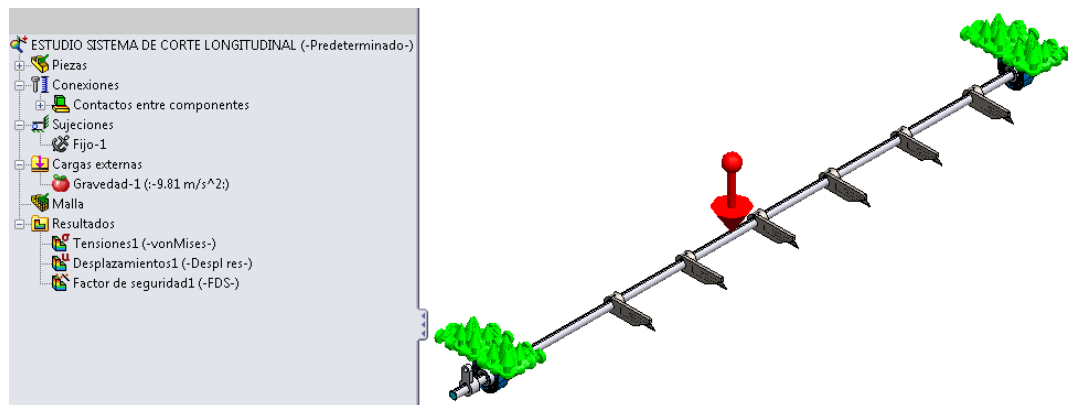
Asignación de cargas y restricciones - sistema de corte longitudinal.
